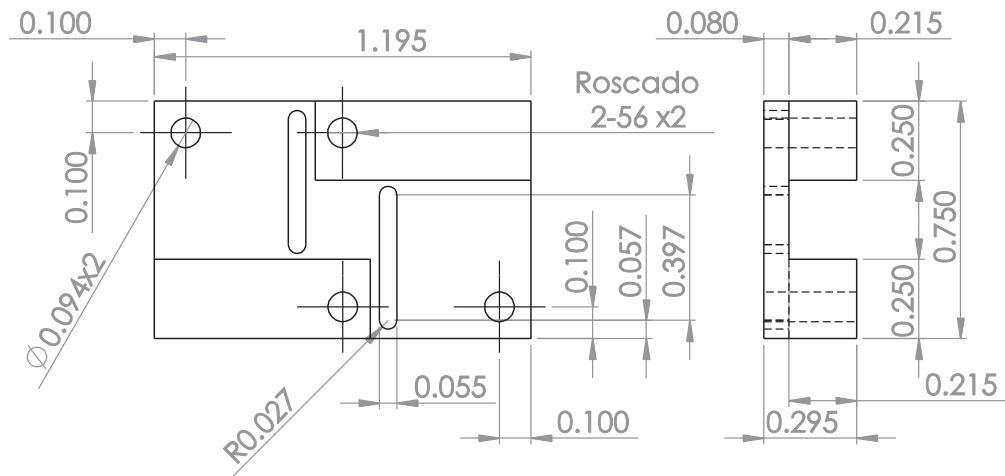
Dimensiones de la base inferior del manipulador M2.
